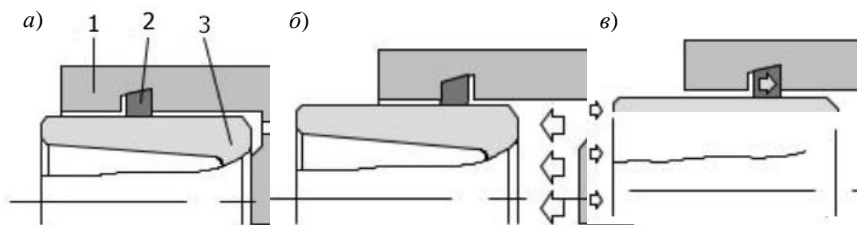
Автоматическая регулировка зазора в дисковом тормозном механизме
